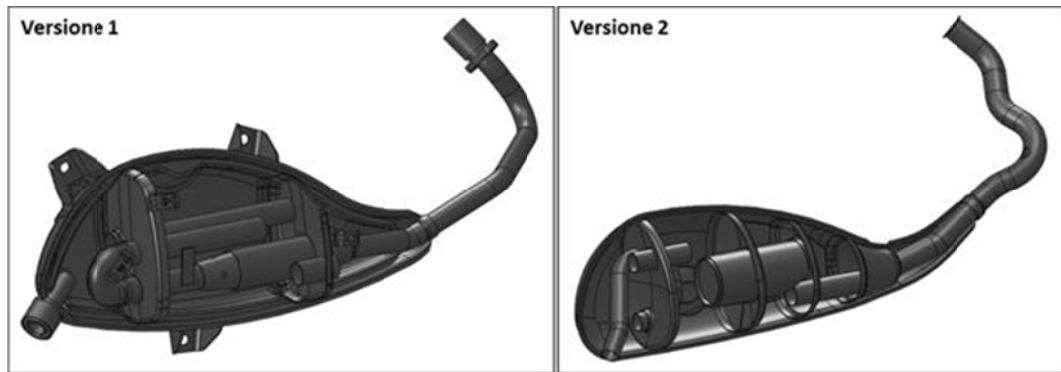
CAD del collettore di scarico e del silenziatore nella versione motore 1 e nella versione motore 2
